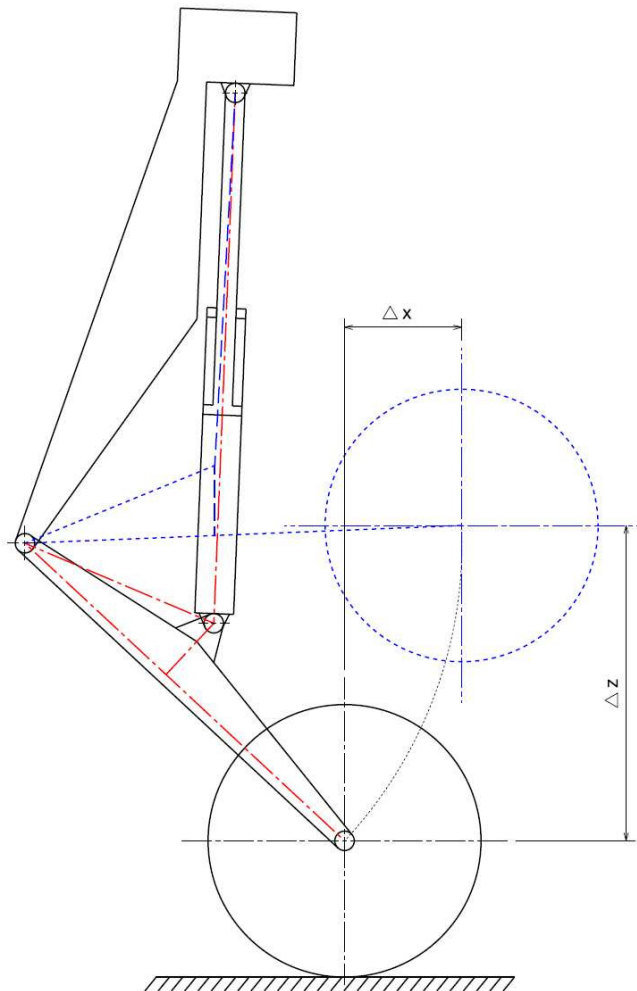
Skizze der Kinematik des Schwinghebelfahrwerks
